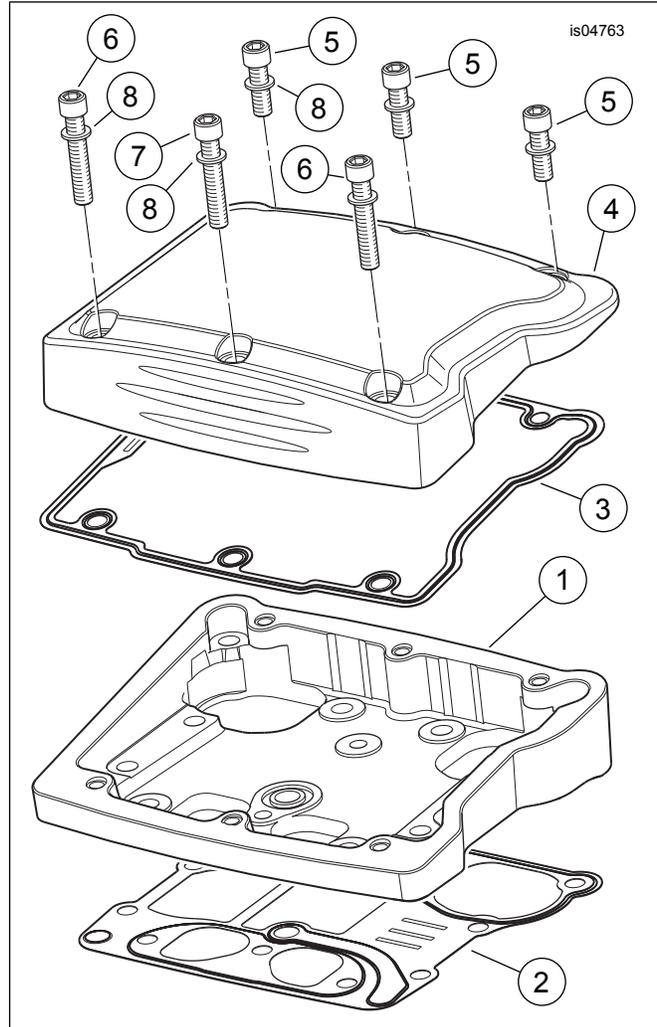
Pièces détachées : kit de couvercle de boîtier de culbuteur billeterie forgée
